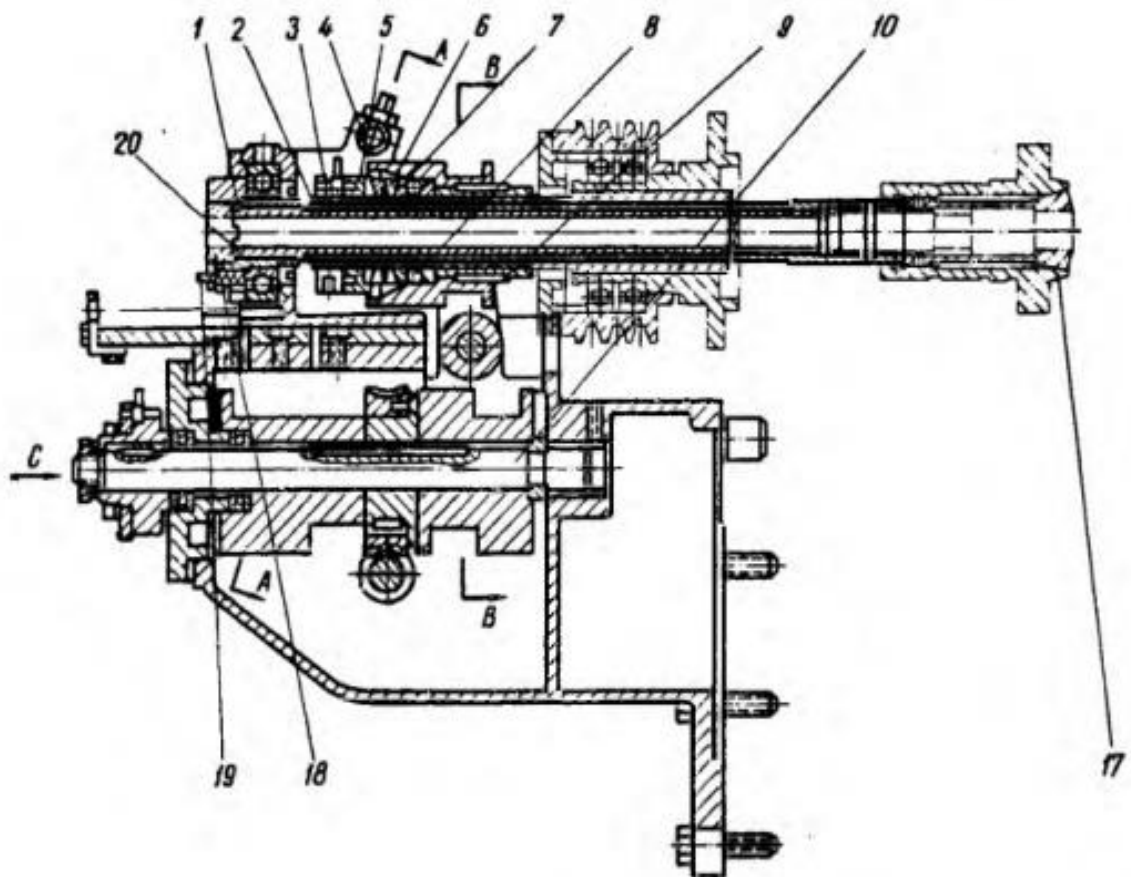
Механізм подачі і затиску прутка: 1- труба подачі; 2-труба затиску; 3-гайка; 4-штопорний гвинт; 5-регулююче кільце; 6-пружний компенсатор; 7-сепаратор; 8-кулька; 9-муфта; 10-кулачковий вал; 17-шпонка; 18-направляюча втулка 25Н.П27.031-034; 19-штифт; 20-повзунка подачі.
